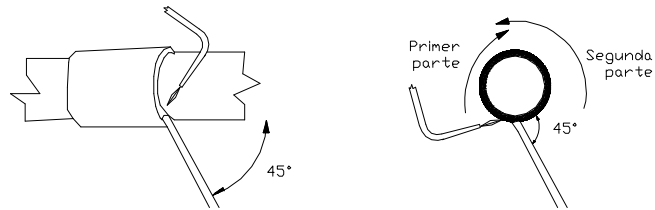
Posición de soldadura de cobre en copa hacia arriba
